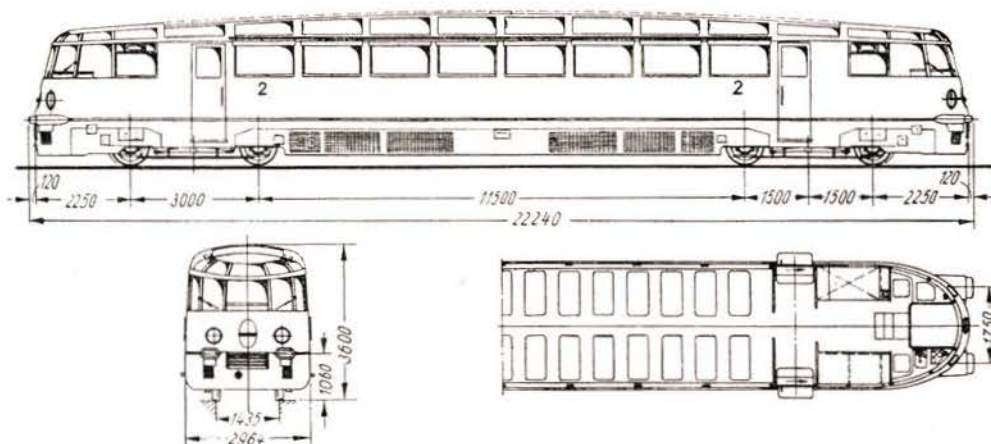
Maßskizze des dieselhydraulischen Aussichtstriebwagens
